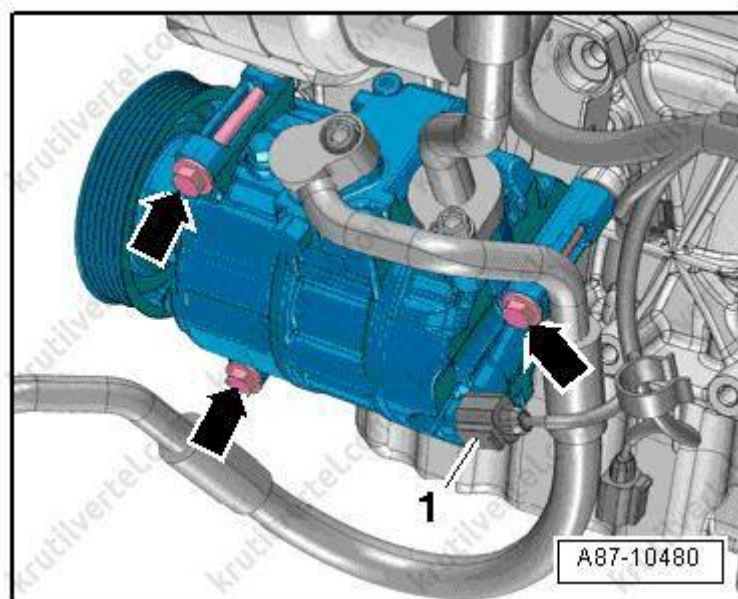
Демонтаж компресора кліматичної установки
